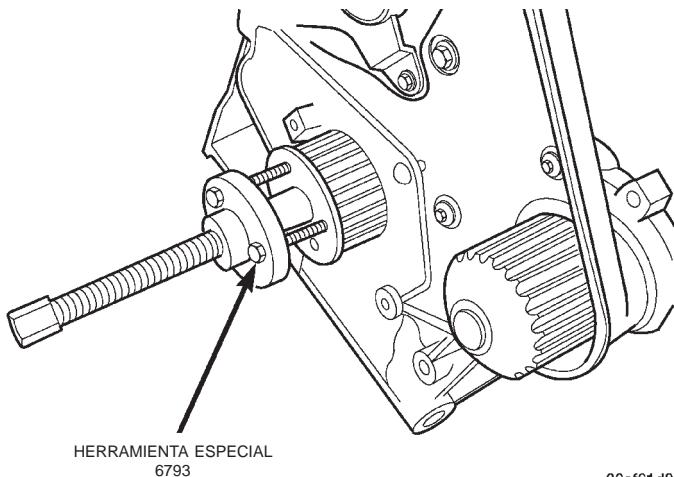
Rueda dentada del cigüeñal—Desmontaje
